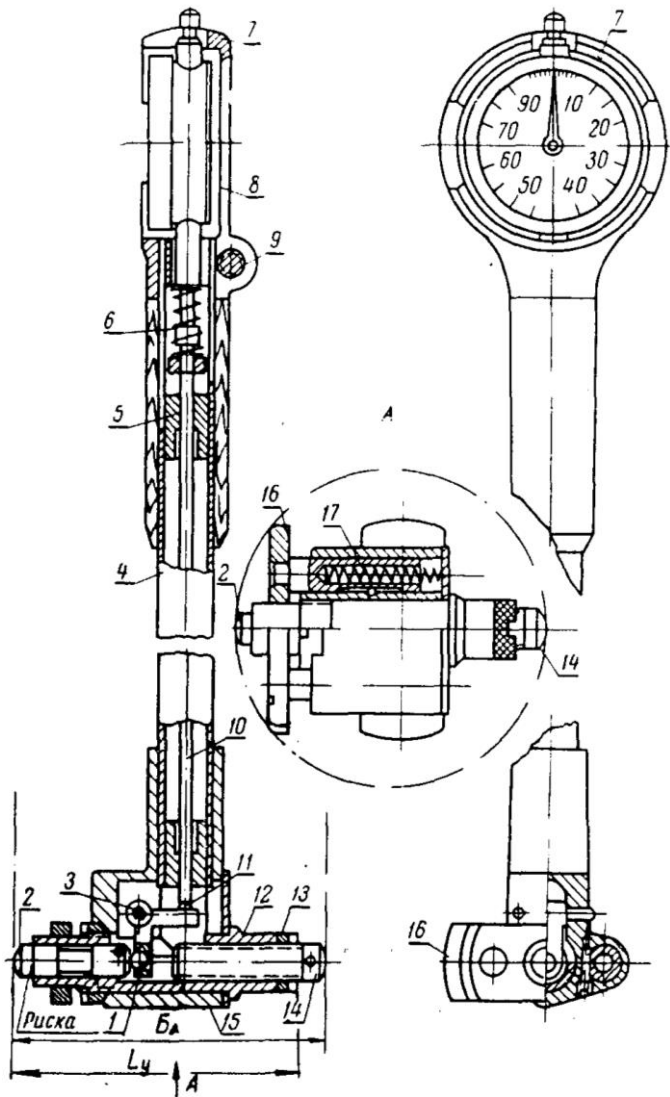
Индикаторный нутромер с рычажной передачей
